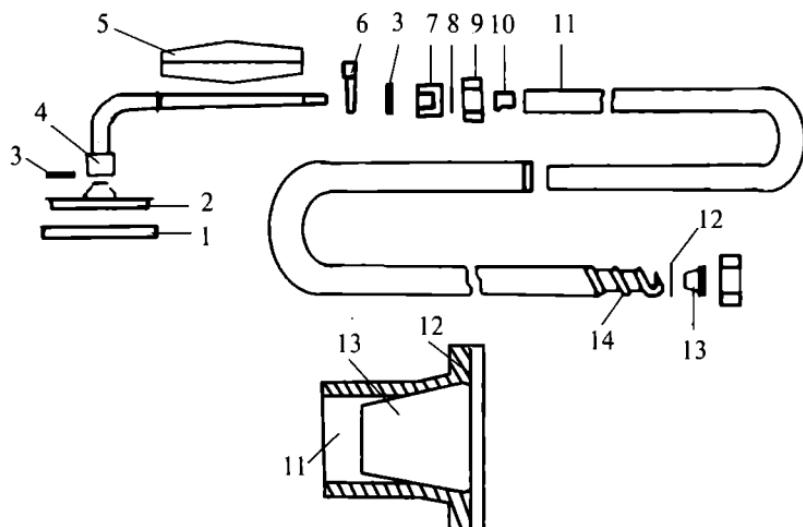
Гибкий резиновый шланг с душевой сеткой: 1 — резиновое кольцо; 2 — душевая сетка; 3 — уплотнение; 4 — остиг; 5 — рукоятка; 6 — петля; 7 — специальная гайка; 8 — резиновая прокладка; 9 — накидная гайка; 10 — латунный ниппель; 11 — резиновая трубка; 12 — пластмассовая или латунная шайба; 13 — пластмассовый ниппель; 14 — хромированная латунная спиральная оболочка
